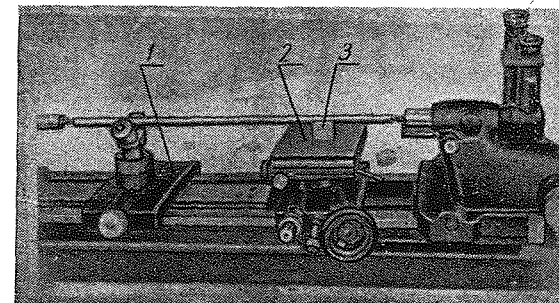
а. Вид измерительной машины с расположением опор (люнет и стола) для цилиндрической концевой меры
